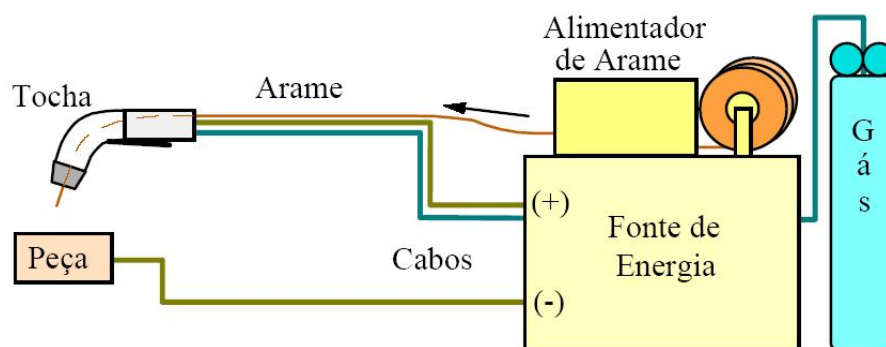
Equipamento básico para a soldagem MIG/MAG
